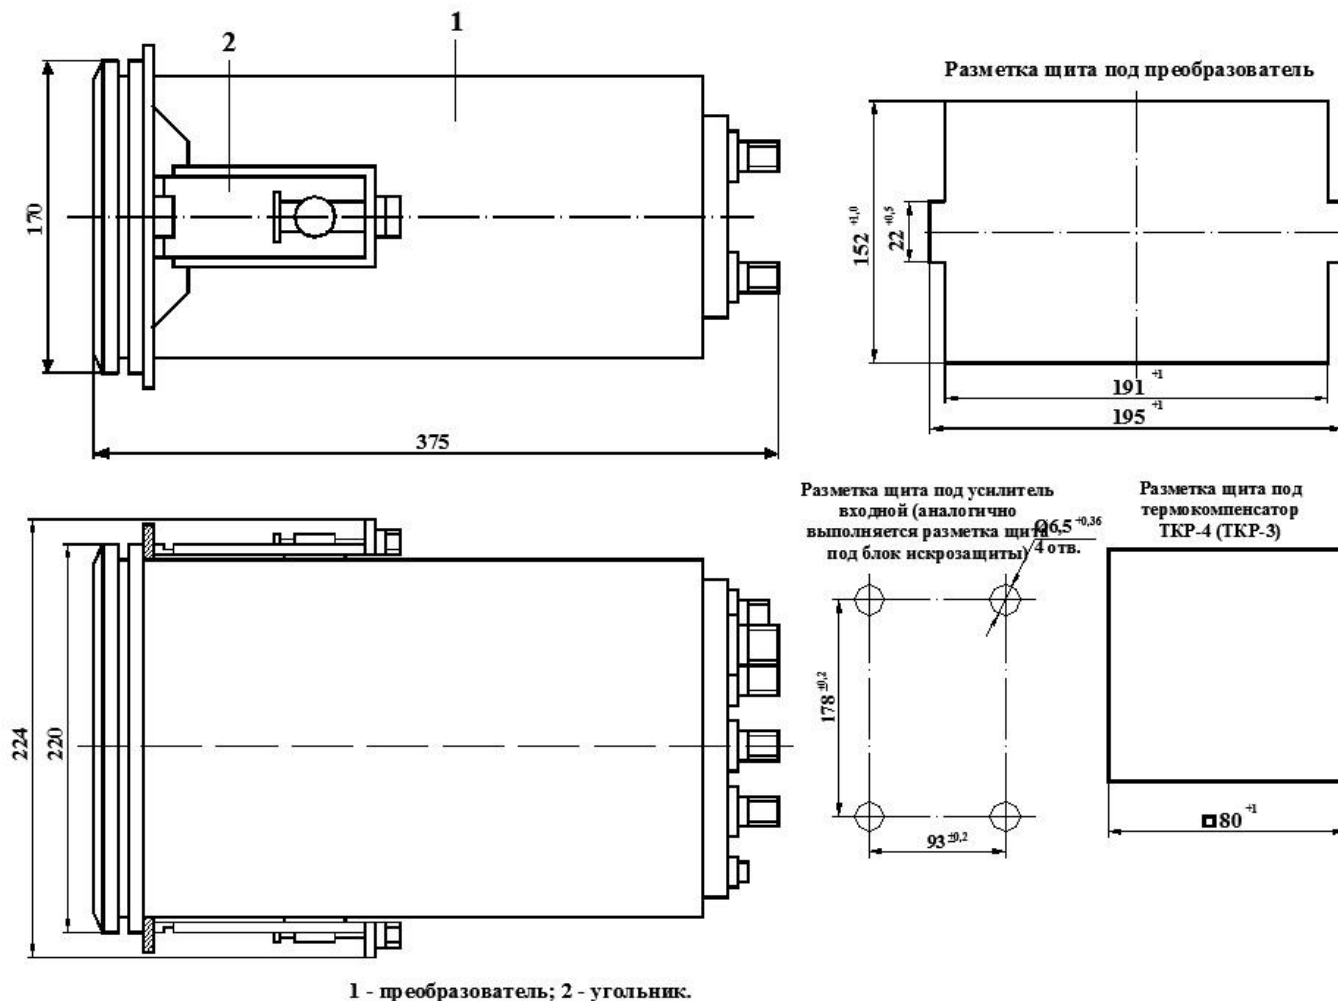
Крепление преобразователя, входного усилителя и блока искрозащиты
